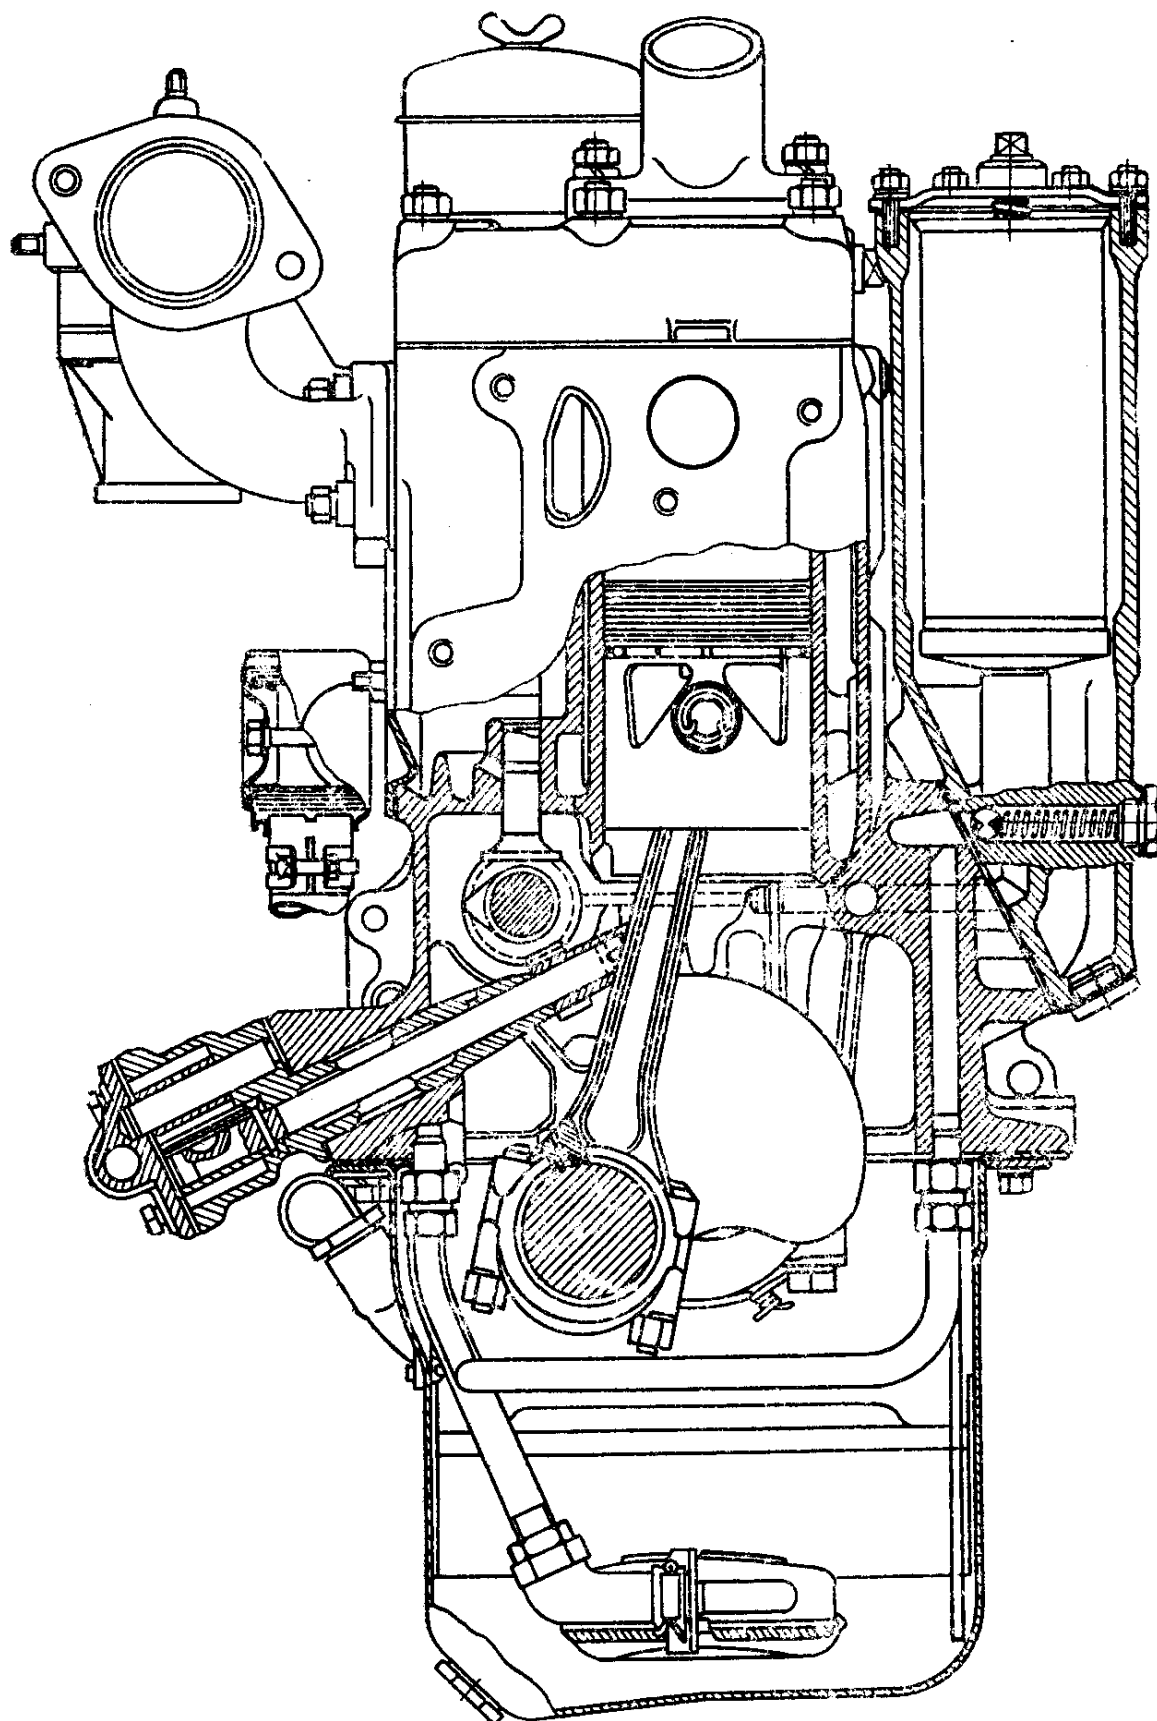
Поперечный разрез двигателя ГАЗ-202
